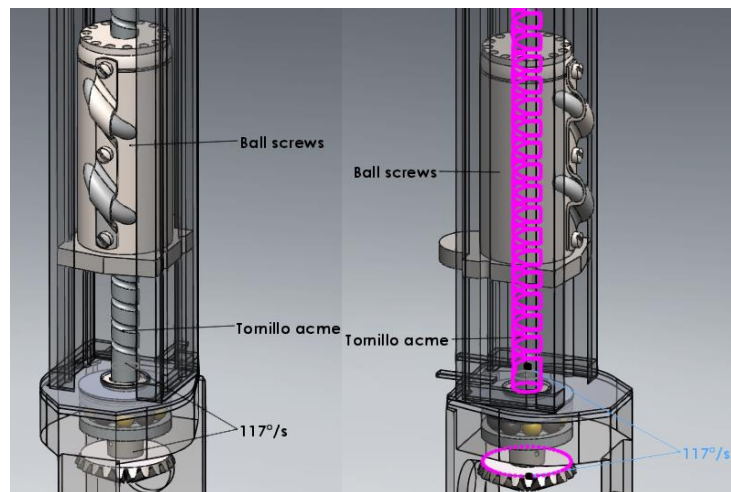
Diseñomecánico de la relación tuerca-tornillo. Fuente propia.
